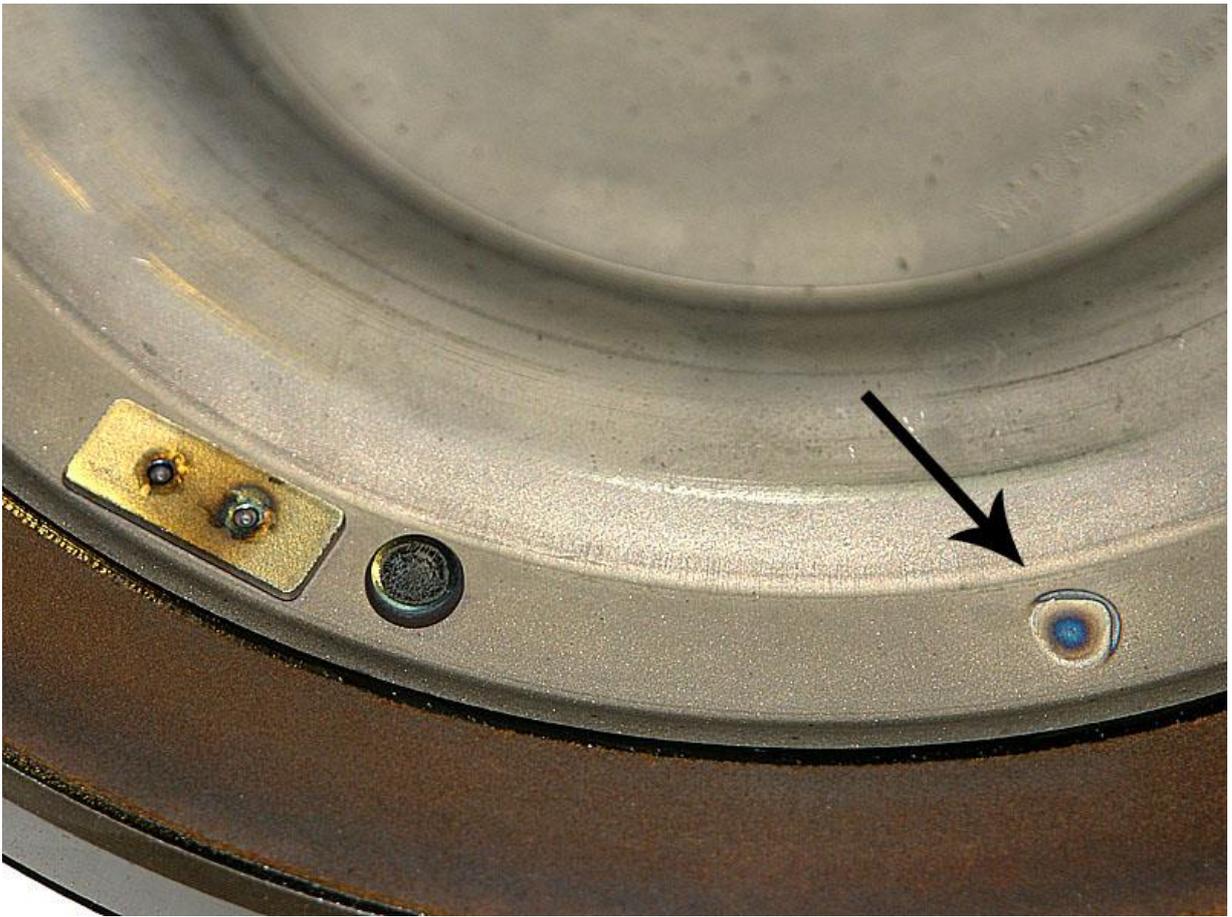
Место точечной сварки оторвавшегося балансировочного грузика поршня блокировки ГДТ.
